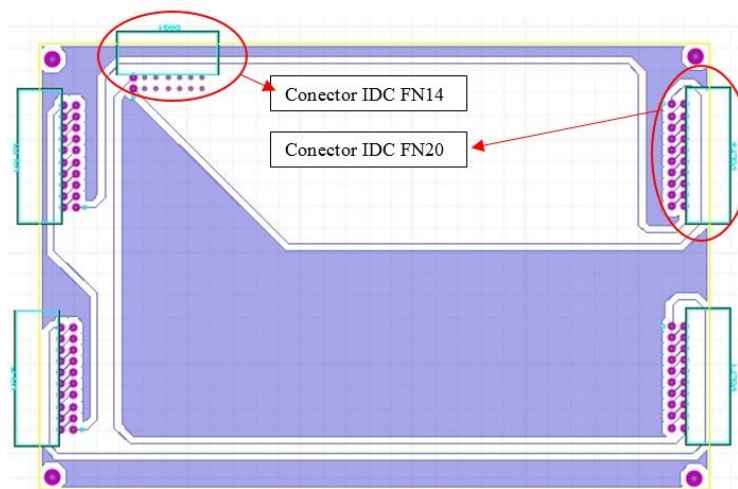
PCB diseñado para la conexión en serie de las 40 CCM
